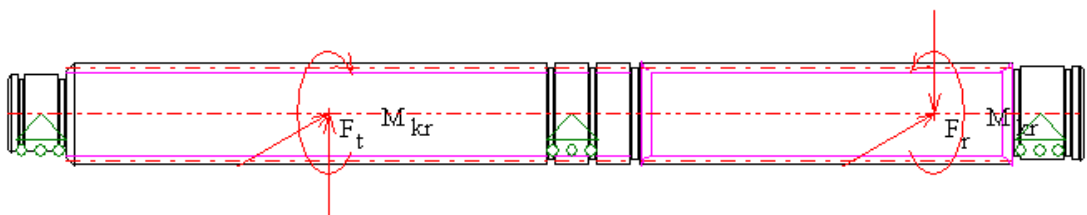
Конструктивна схема вала в модулі APM Shaft
